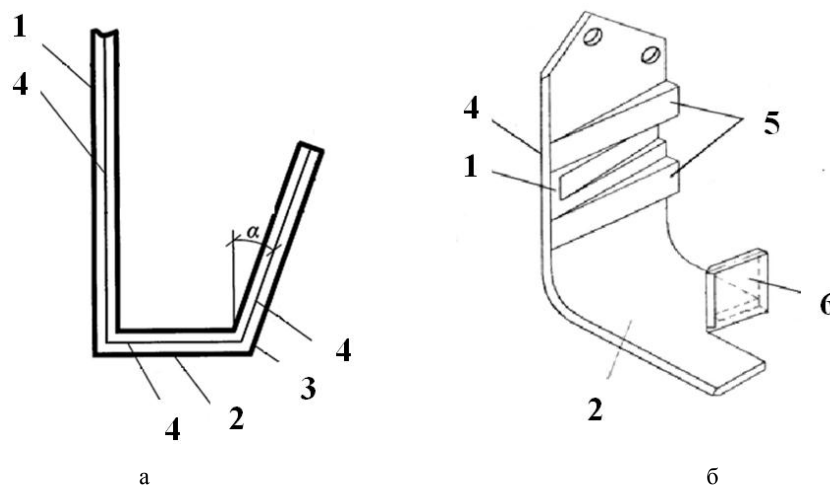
Виды ножей: а – L-образный; б – пластинчатый: 1 – стойка; 2 – крыло; 3 – отогнутая часть; 4 – режущая кромка; 5 – рыхлительный элемент в форме клиновидных расширяющихся выступов; 6 – рыхлительный элемент крыла
